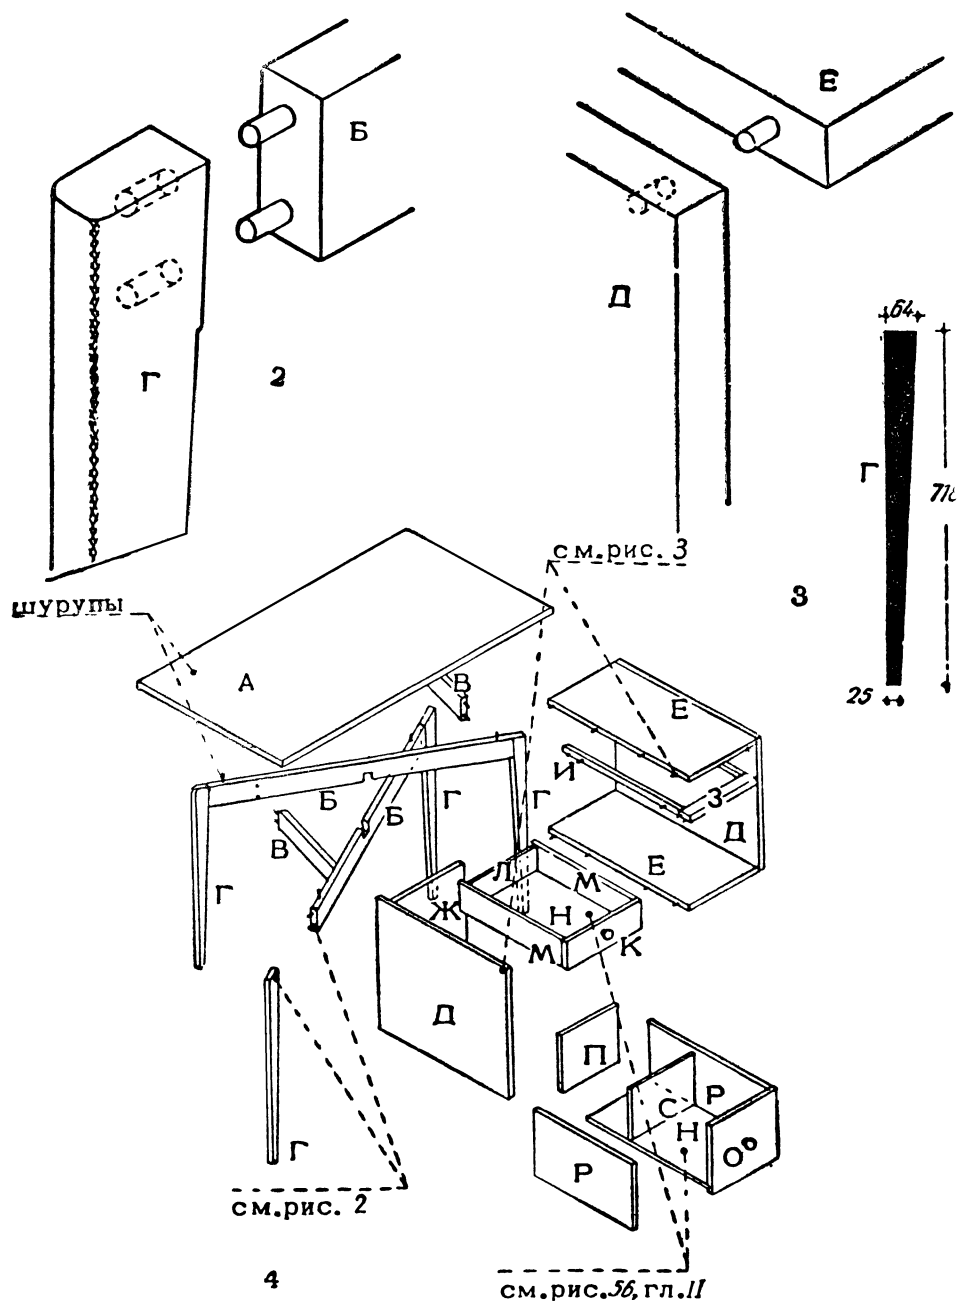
4. 2 — эскиз соединения ножки с царгой; 3 — деталь ножки и эскиз соединения боковой стенки с верхним полком тумбы; 4 — эскиз сборки деталей.
